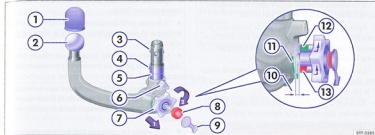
Vue d'ensemble : boule amovible du dispositif d'attelage.
